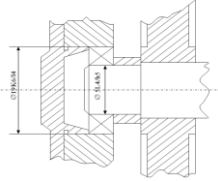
Эскиз сопряжения подшипника с валом и корпусом
